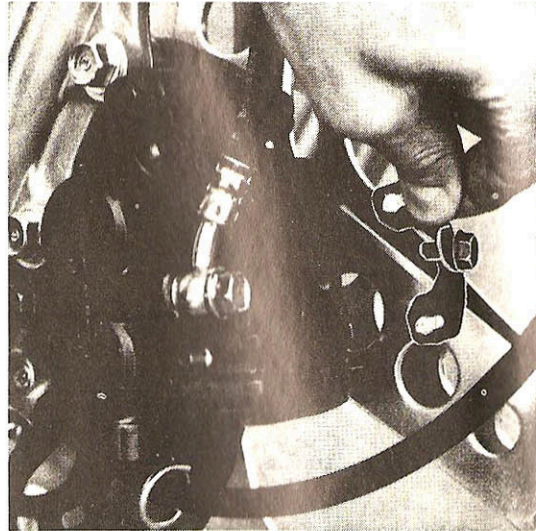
Dépose de la plaque de calage latéral des axes des plaquettes (Photo RMT)
